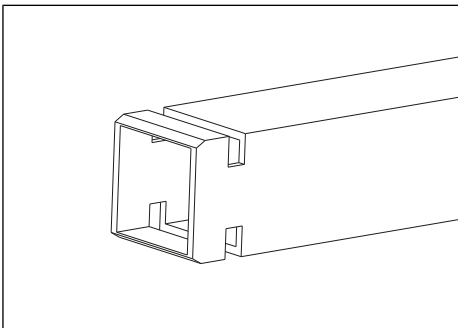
Scanalature sul supporto trasversale Multi Wall
